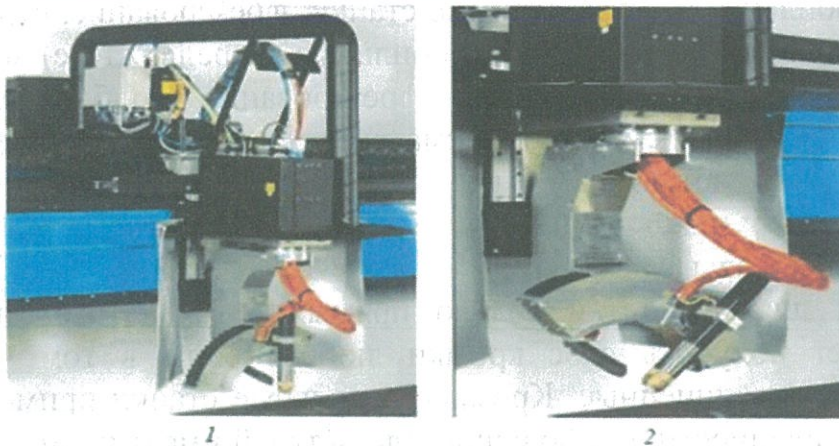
Поворотная плазменная режущая горелки машин термической резки в поворотном шаровом шарнире:
